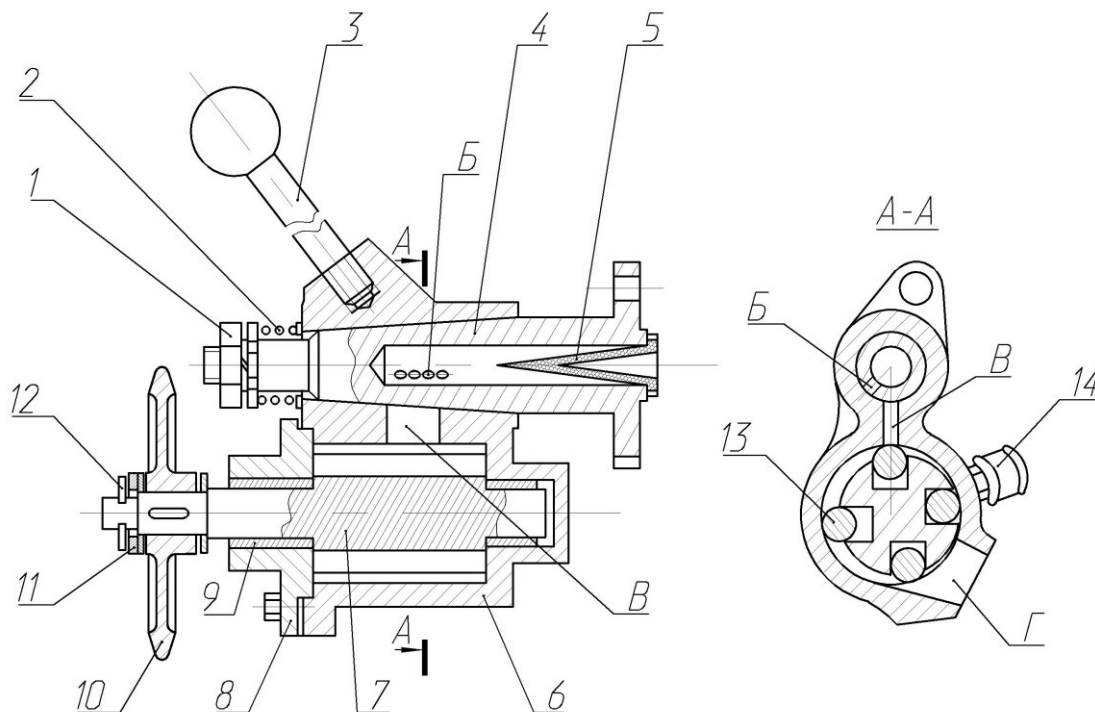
Шиберный роликовый насос мотопомпы МП-600А: 1 - гайка; 2 - пружина; 3 - рукоятка; 4 - пробка-ось (выполняет функции вакуумного крана); 5 – сетка (фильтр); 6 - корпус; 7 - ротор; 8 - крышка; 9 - подшипники скольжения; 10 - фрикционное колесо; 11 - шайба; 12 -
